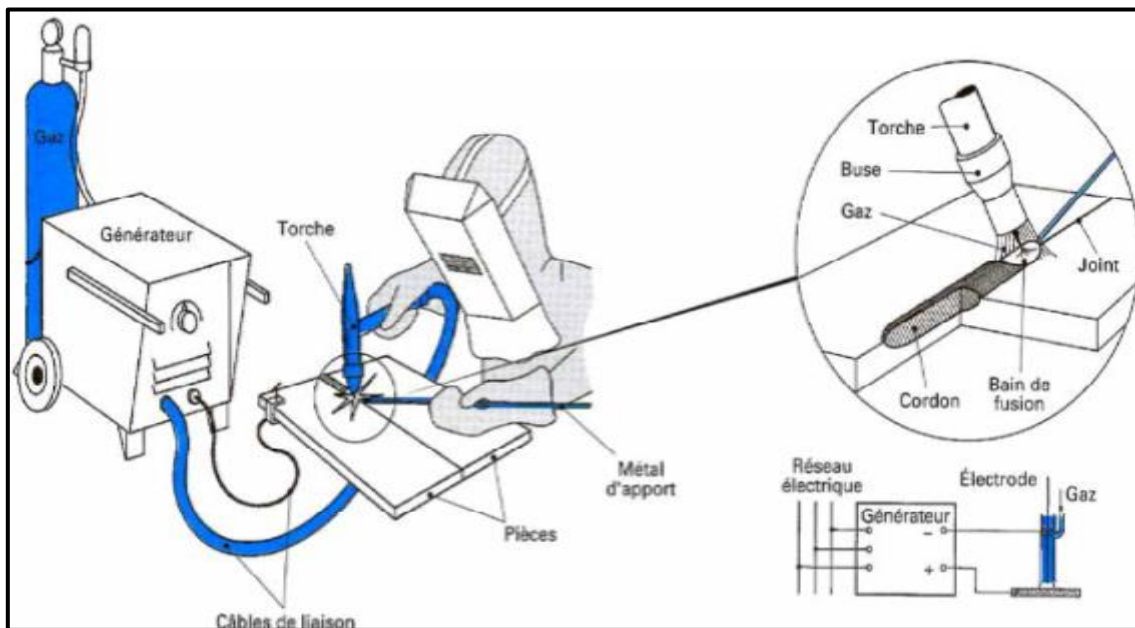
Principe de la procédé de soudage GTAW [30].
